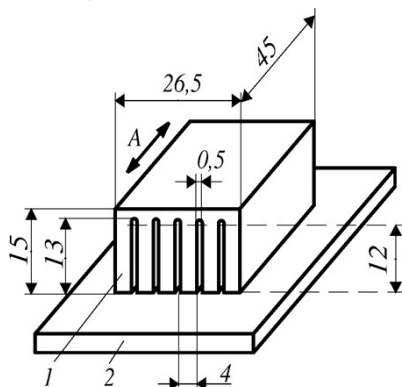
Схемы изготовления пьезодатчиков из кварца:
